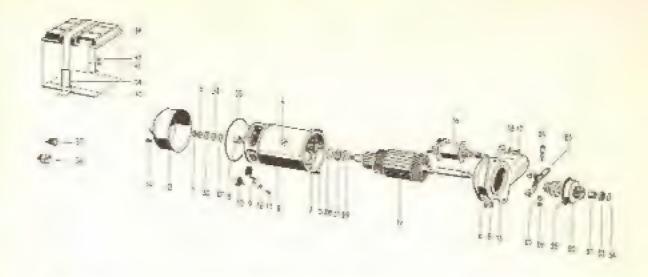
S - O motor de partida Bosch desmontado e a caixa da bateria
